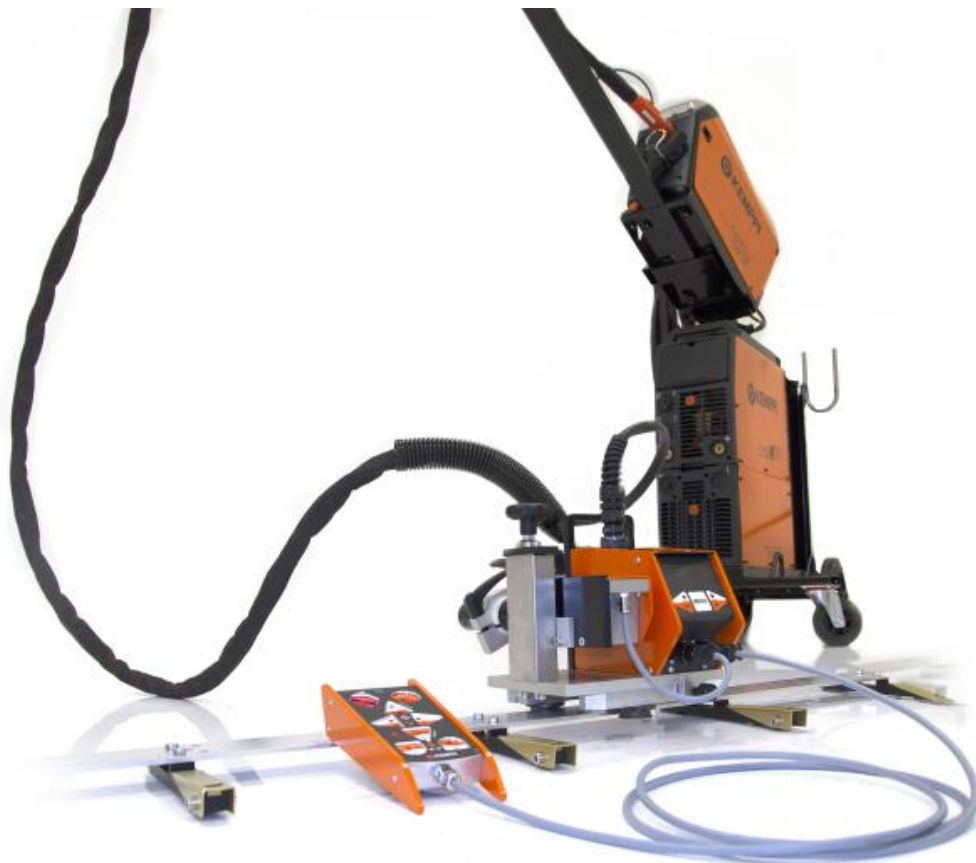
Рейкова зварювальна каретка Kemppi A3 MIG Rail System 2500 [21]
